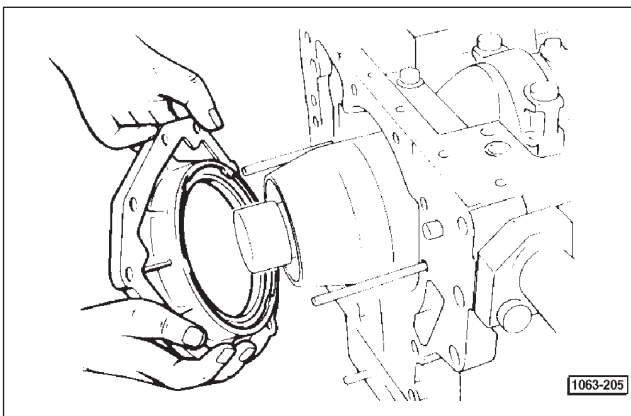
Den Flansch unter Verwendung eines Schutzringes montieren. Hinweis - Der im neuen Flansch eingesetzte Ring darf absolut nicht geschmiert werden. Die Befestigungsschrauben mit Dichtmasse bestreichen, die Kupferscheiben zwischenlegen und mit dem auf Seite 98 angegebenen Anzugsdrehmoment festschrauben.
